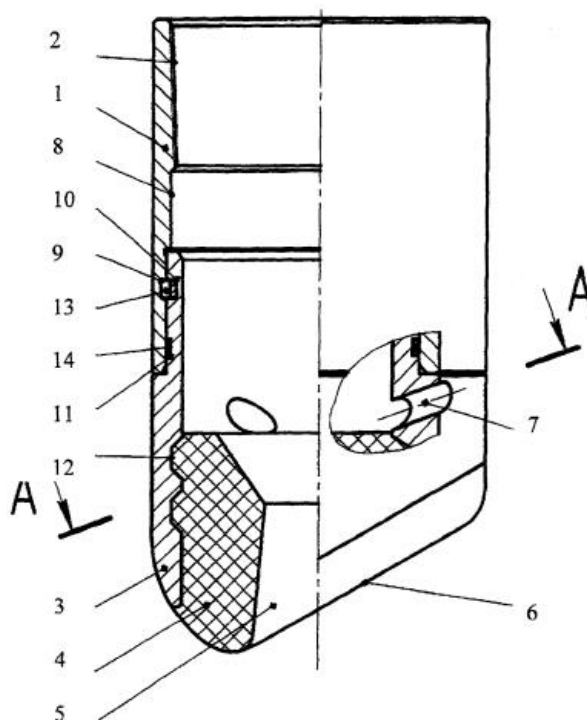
Колонный башмак: 1 – корпус; 2 – муфтовая резьба; 3 – втулка; 4 – направляющая насадка; 5 - центральный канал; 6 – скос; 7 – боковые отверстия; 8 и 9 – кольцевые проточки; 10 и 11 – наружные кольцевые проточки; 12 – внутренние кольцевые проточки; 13 - пружинный фиксатор; 14 – антифрикционное кольцо
